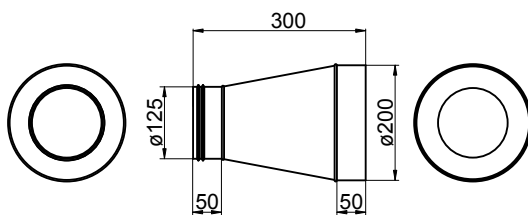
Dimensions de raccord de transition DN125 (dimensions en mm)
